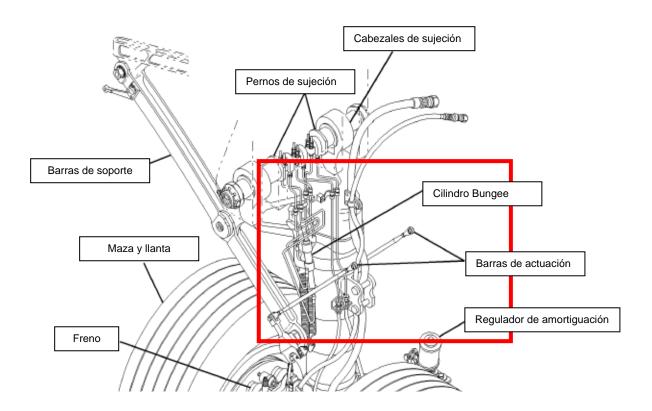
se ilustran los componentes que se deben remover para realizar la inspección.
